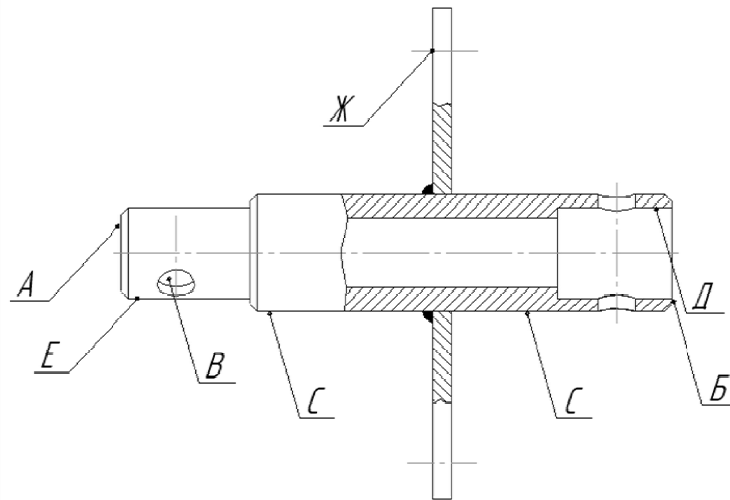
Деталь «Опора ротатійного розпушувача ліва РР.034.22.12»
